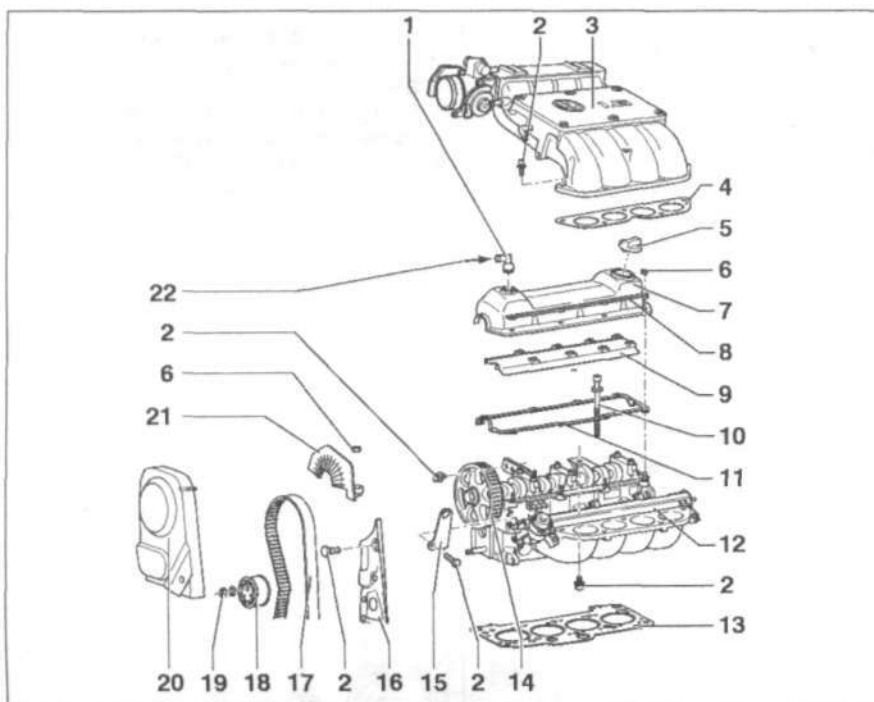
Головка блока цилиндров двигателя AFT:
